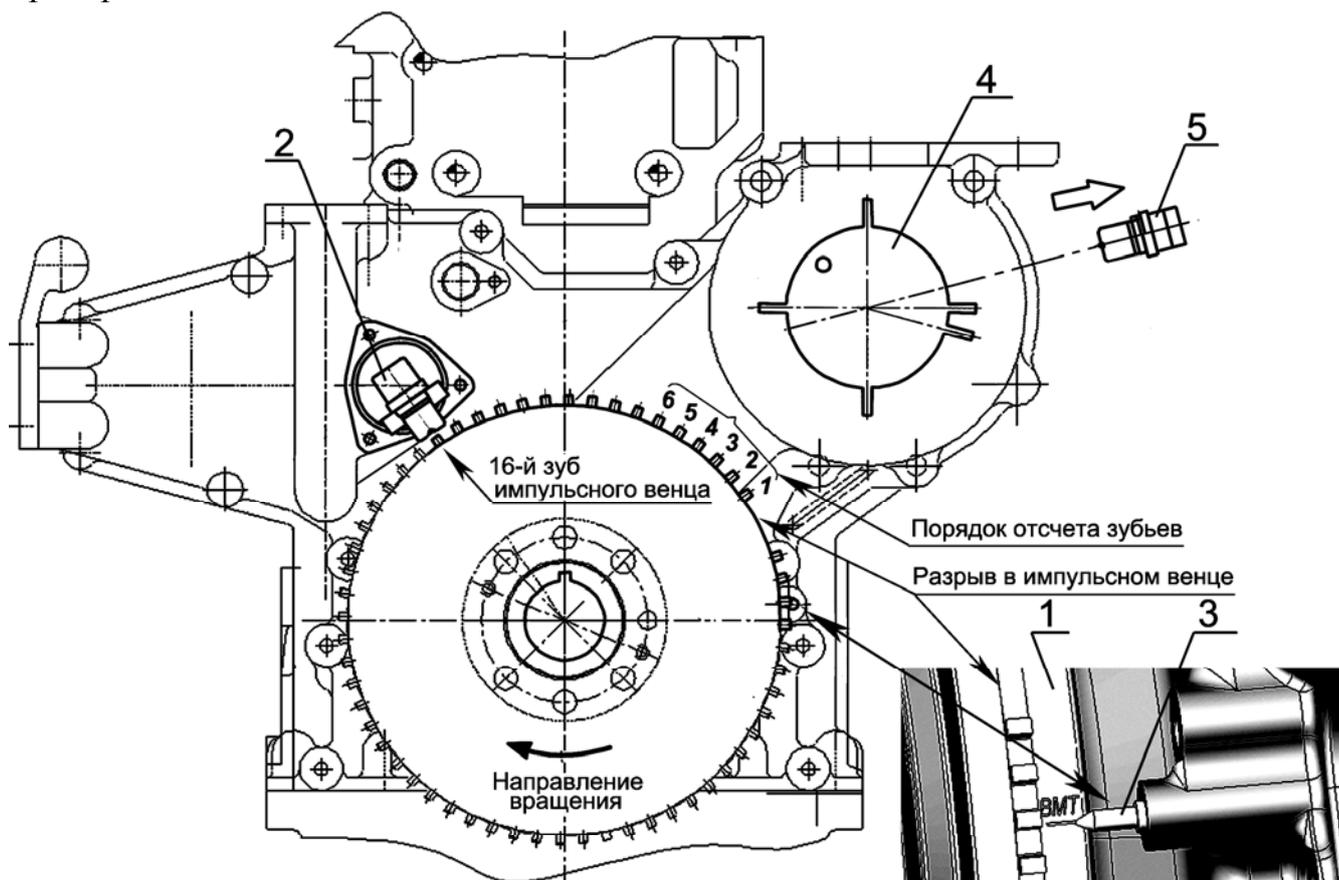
Приспособление для фиксации импульсного венца шестерни привода топливоподкачивающего насоса.
